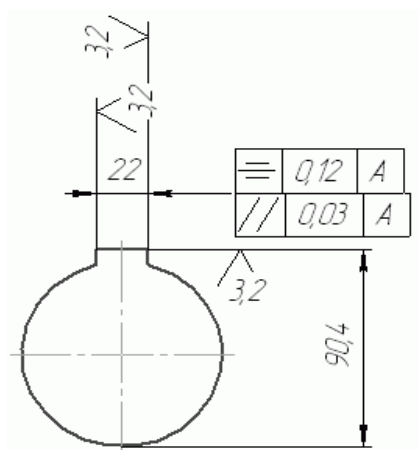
Размеры, шероховатость и допуски профиля отверстия в ступице колеса
